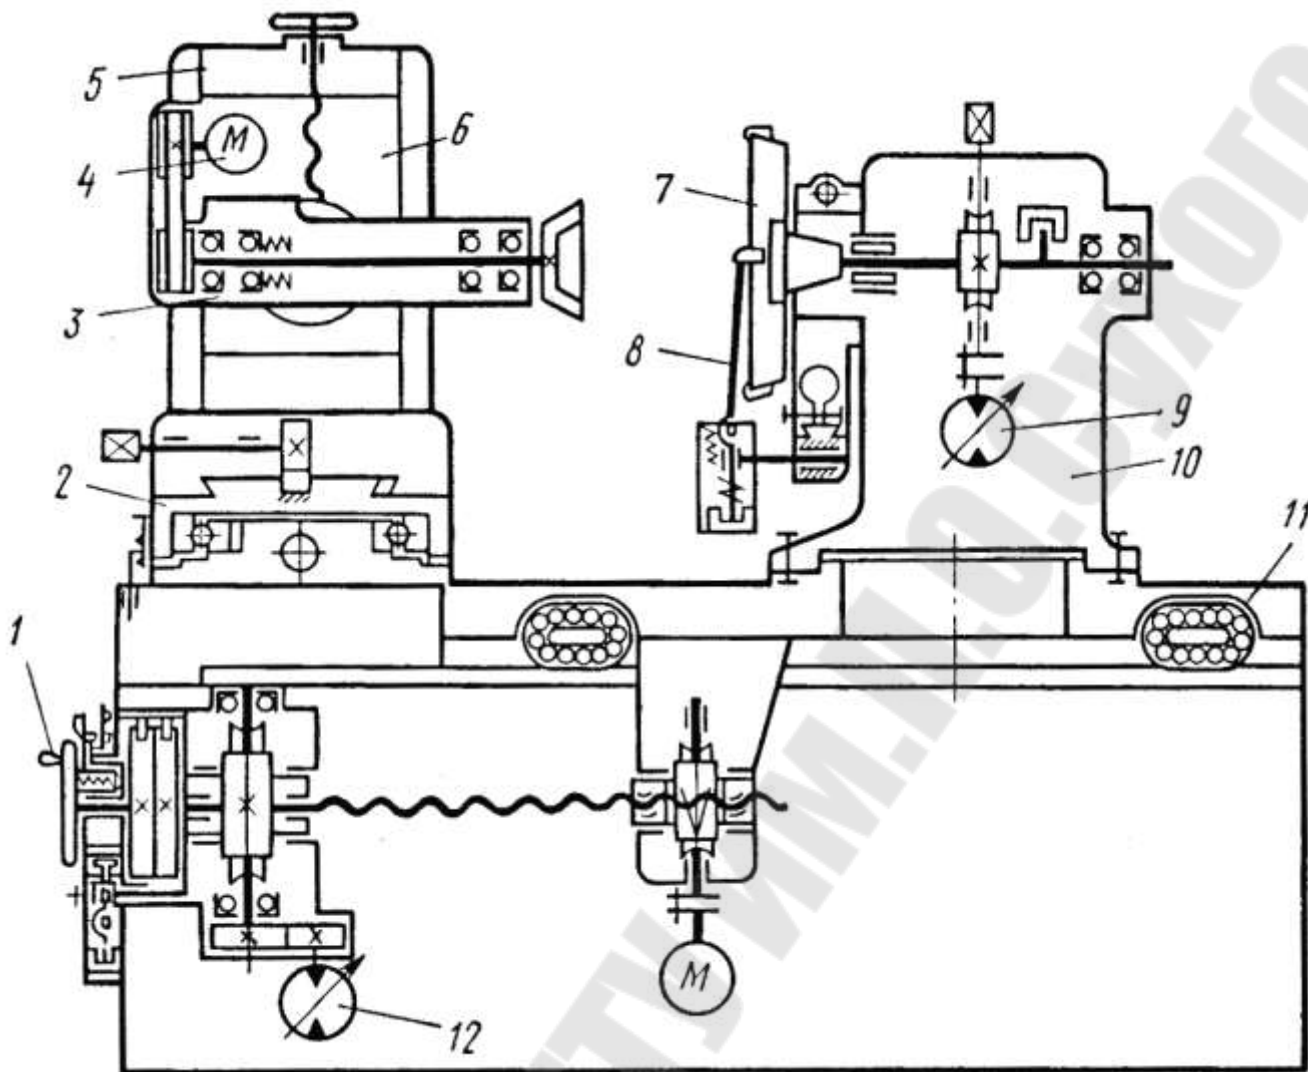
Принципиальная схема полуавтомата модели 3Б667Ф2 для заточки торцовых фрез: 1 – маховичок; 2 – стол; 3 – шлифовальная бабка; 4 – электродвигатель; 5 – колонна; 6 – салазки; 7 – фреза; 8 – упорка; 9, 12 – гидродвигатели деления и подачи; 10 – бабка изделия; 11 – суппорт
